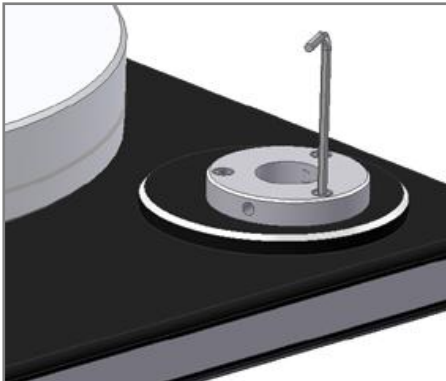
Abmessungen zur Montage des Klemmrings bei Fremdlaufwerken
